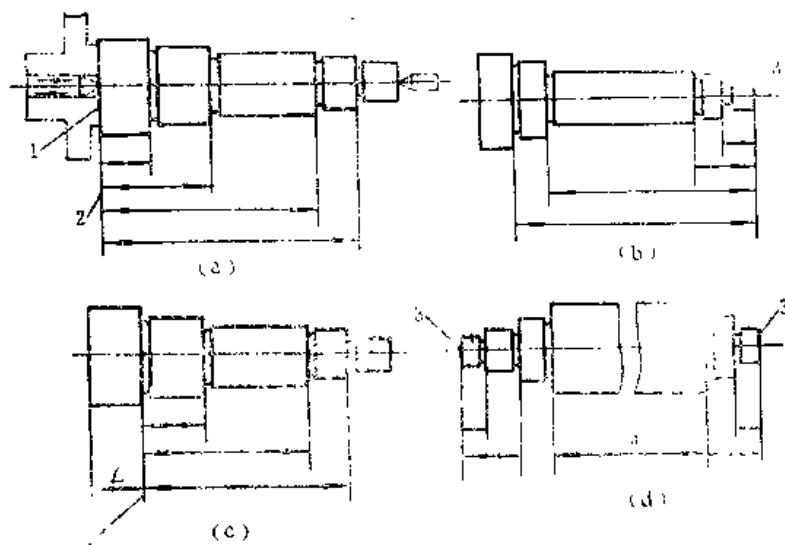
在多刀车床上加工阶梯轴的尺寸标注
